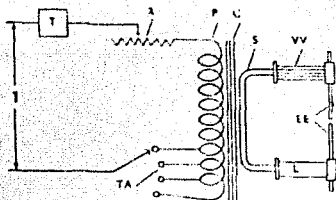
El circuito eléctrico de un soldador de soldadura de punto. P, arrollamiento primario del transformador; C, núcleo del transformador; S, arrollamiento secundario del transformador; T, interruptor regulador del tiempo. Este puede ser simplemente un interruptor mecánico automático, mecánico que opera automáticamente o electrónico. TA, derivación en el arrollamiento primario; R, resistencia variable; VV, soltas deslizables que hacen posible al electrodos superior y también, por un movimiento vertical del mismo. Algunas veces, puede ser parte de un movimiento de sujeción del electrodo superior en este punto cuando se está soldando. L, interruptor de tiempo.
